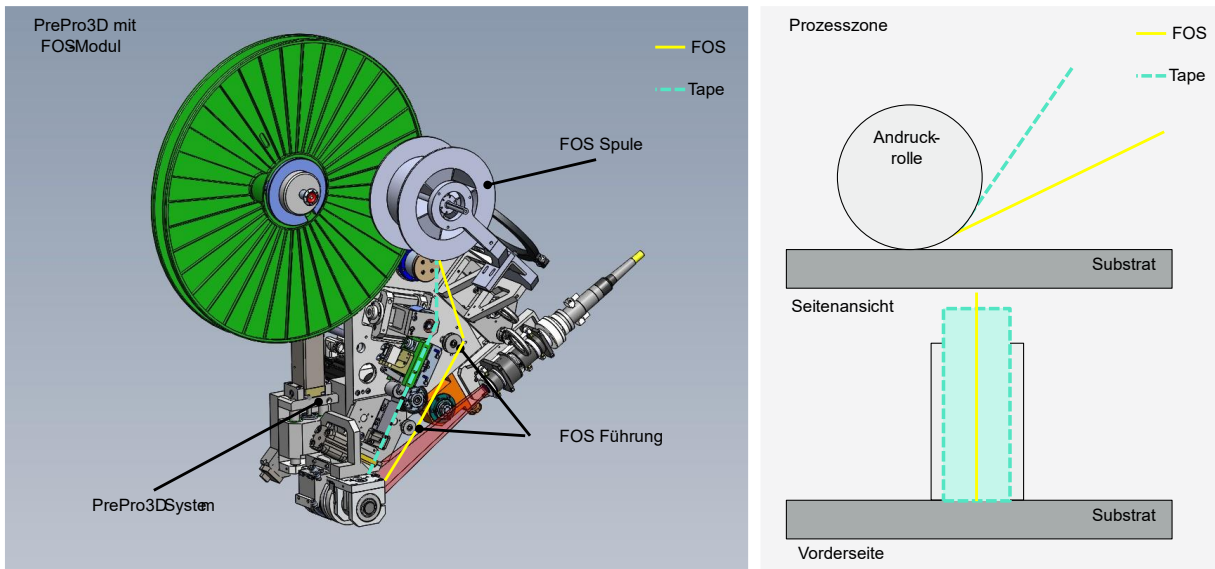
CAD-Design der Maschinenerweiterung (links) und Skizze der Prozesszone (rechts) für die automatisierte Integration faseroptischer Sensoren.
